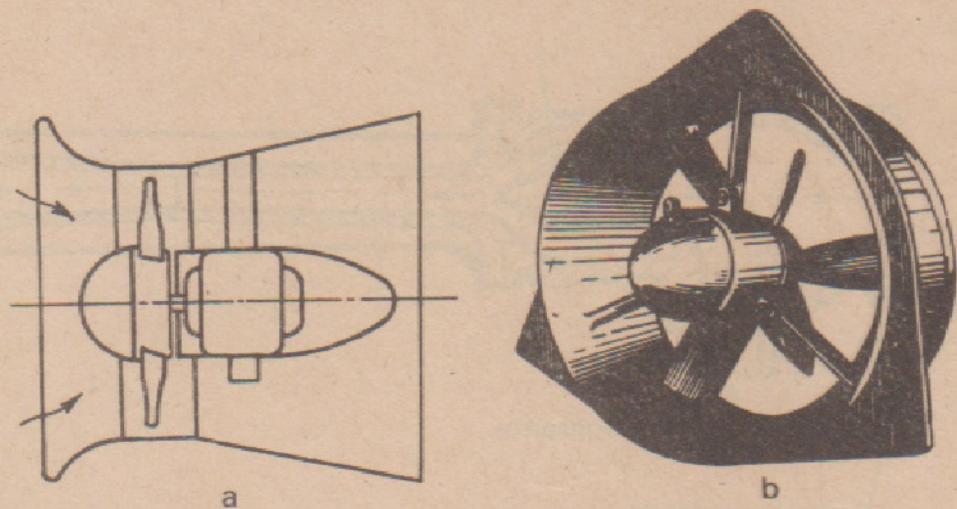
Ventilador axial: a) esquema; b) vista externa
